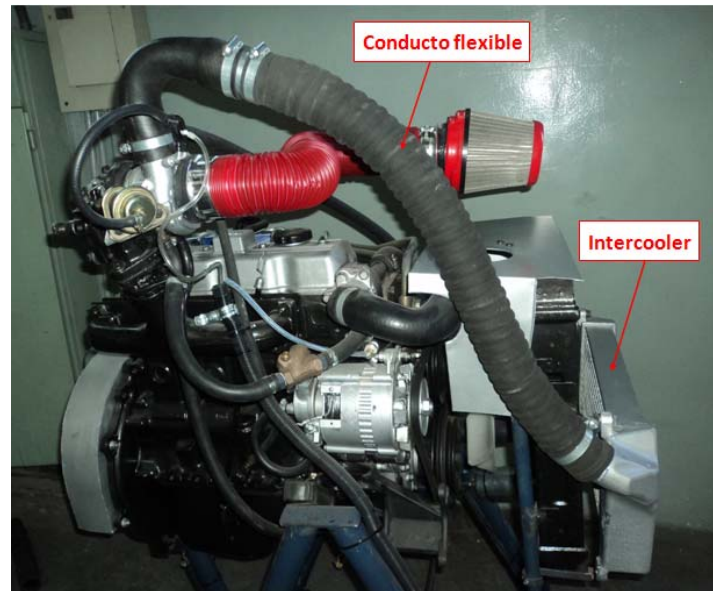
27 Unión del turbocompresor con la entrada del intercooler mediante manguera flexible.
